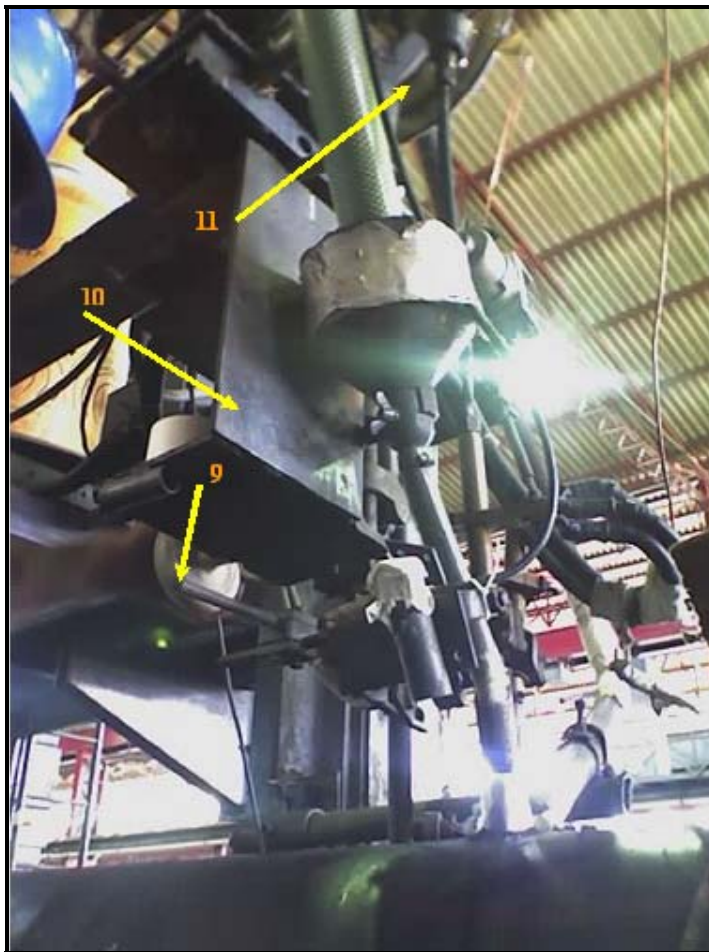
Se observa el cabezal de soldadura en una vista completa
